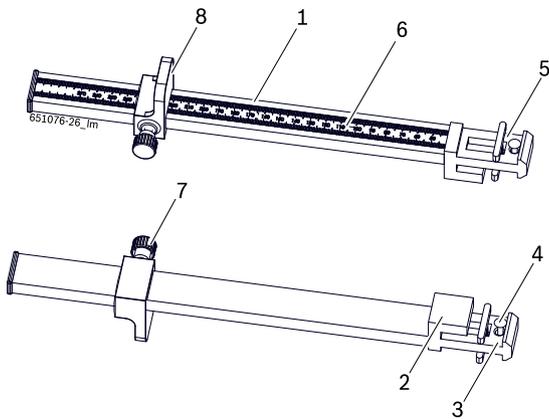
Ручной раздвижной калибр: регулируемый упор для монтажного ручья обода, внизу: неподвижный упор для борта обода
